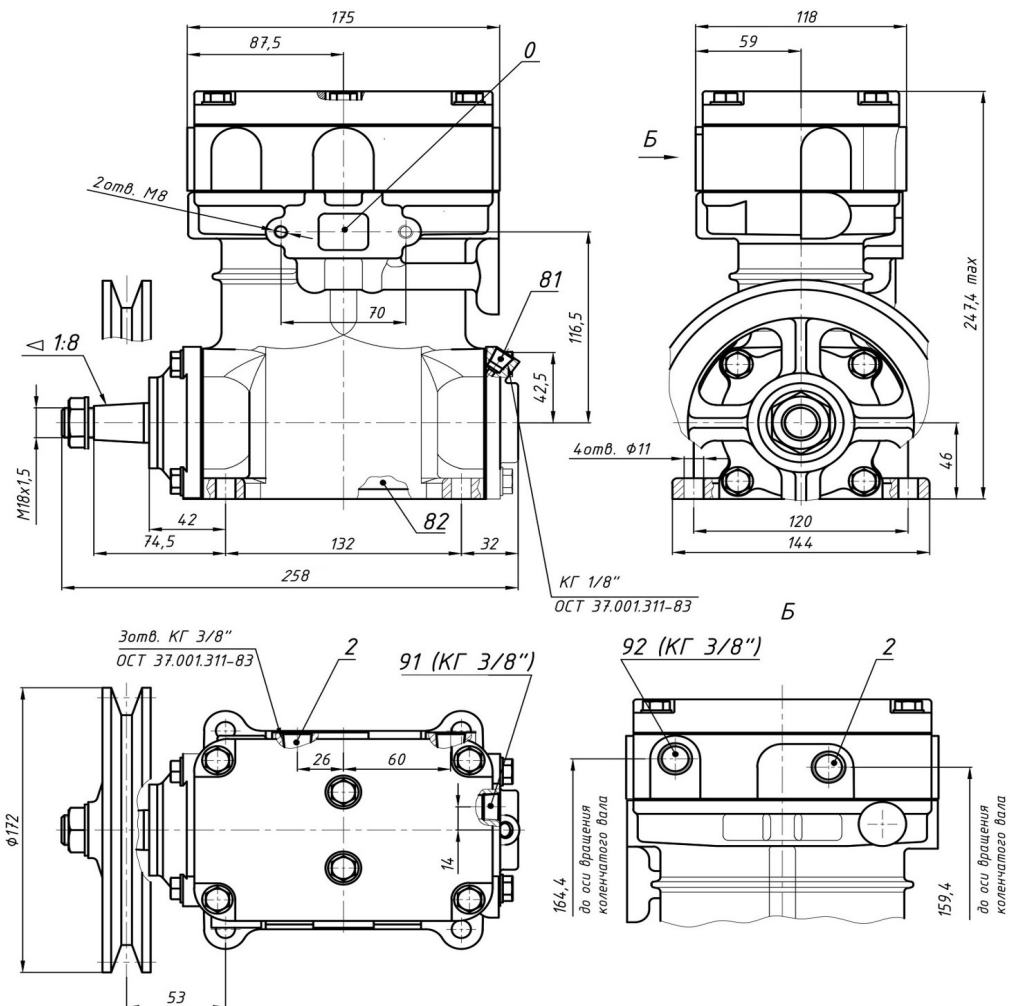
Присоединительные и установочные размеры компрессора АМ.3509012-16.
